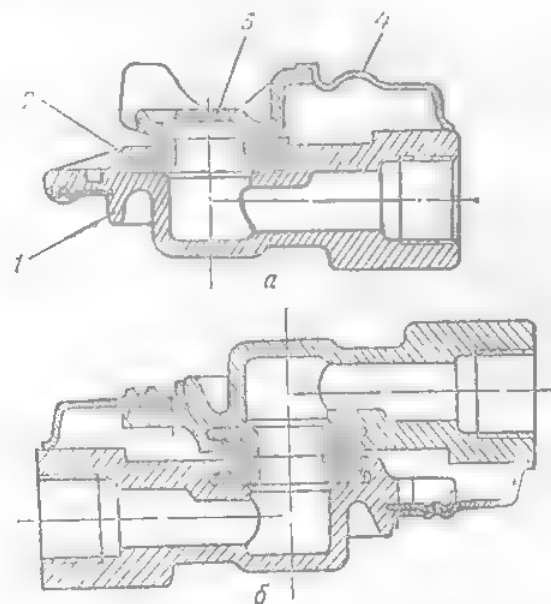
Соединительная головка типа «Палм»: а — соединительная головка тягача; б — соединительные головки тягача и прицепа; 1 — корпус; 2 — уплотнительная прокладка; 3 — крышка; 4 — направляющая
